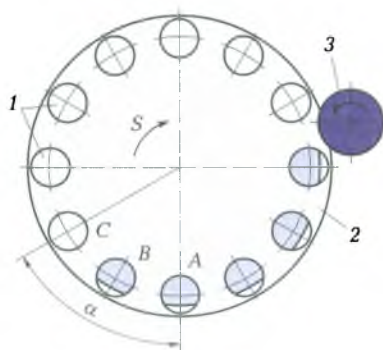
Схема одновременной непрерывной обработки заготовки:
